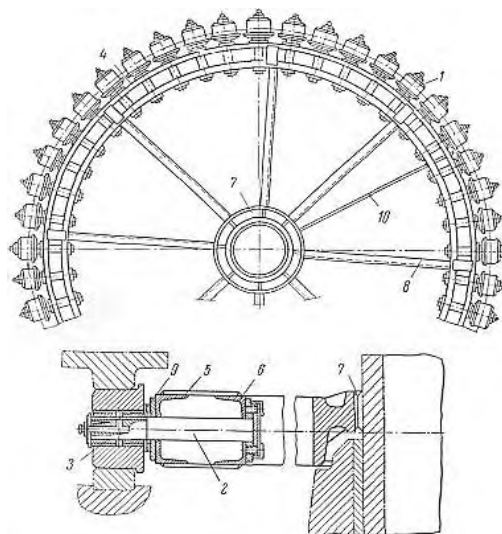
Опорно-поворотное устройство экскаватора ЭКГ-8И
